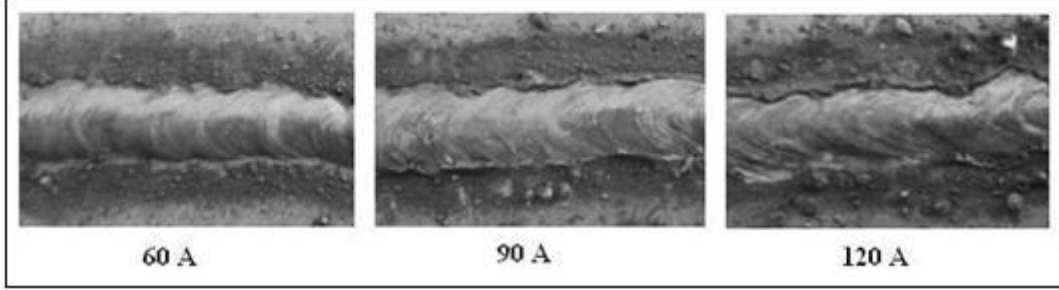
MIG kaynağı ile yapılan kaynak dikişlerinin makro görüntüleri (Macro images of welds with MIG welding)
